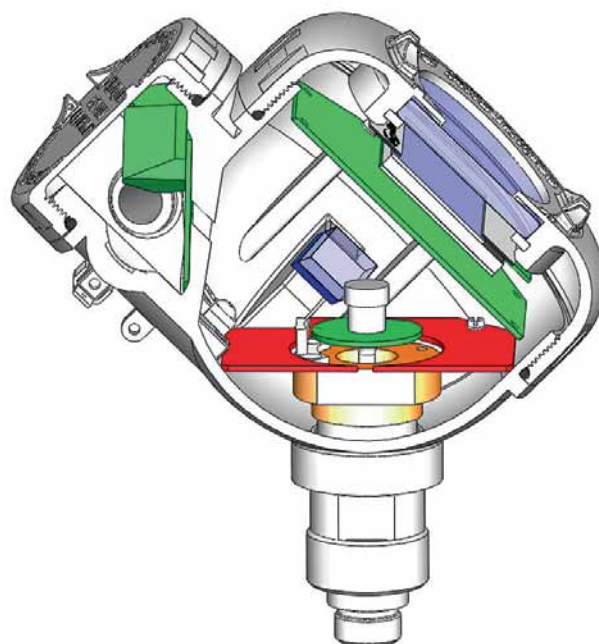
Конструкция основного корпуса полевых приборов с модулем внутреннего активного обогрева (обозначен красным цветом)
